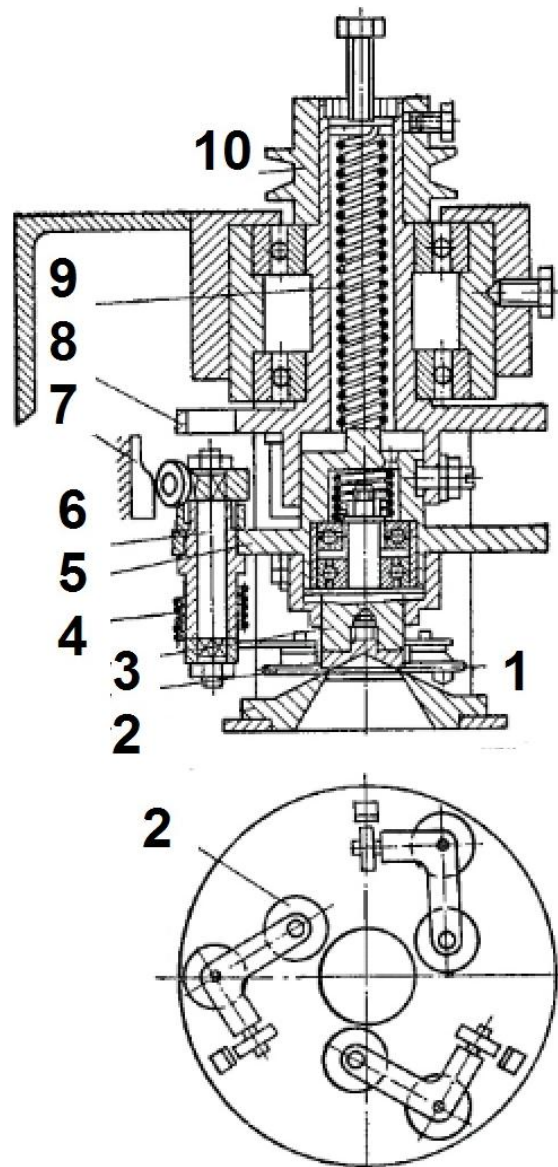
Обкатний роликовий закупорювальний механізм
